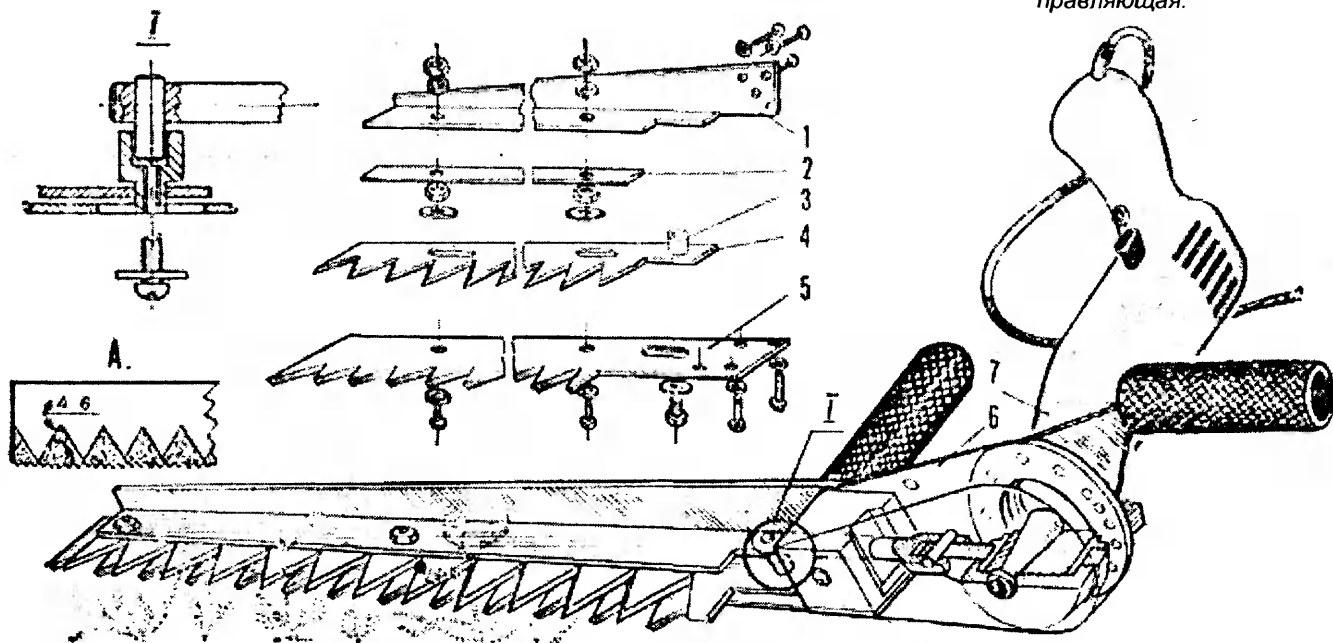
Конструкция косилки и основные детали режущего аппарата:
